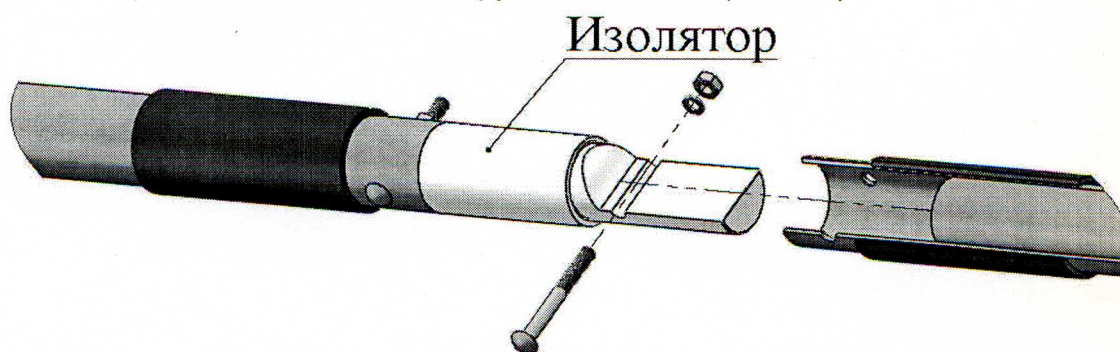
Стыковка левой и правой части элемента №4 20 Mtr Driver на изоляторе.
